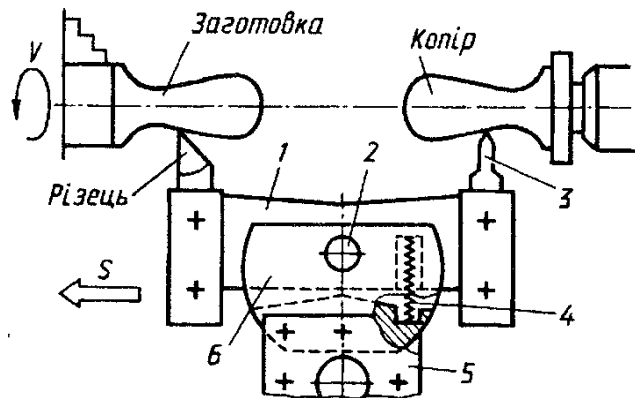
Пристрій Й. П. Гурґаля для обточування фасонних поверхонь: 1 - важіль; 2 - палець; 3 - щуп; 4 - пружина; 5 - різцетримач; 6 - корпус
